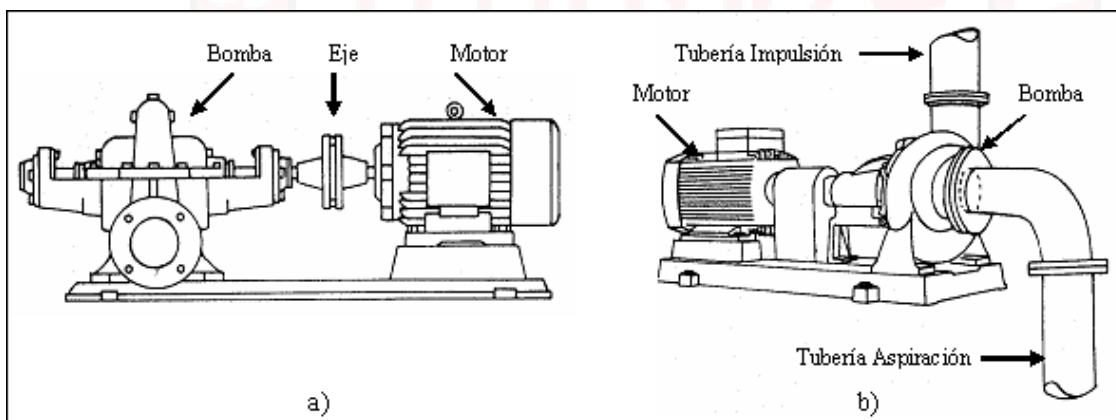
FIGURA Bombas horizontales a) Disposición del grupo motobomba b) Perspectiva grupo motobomba monocelular
